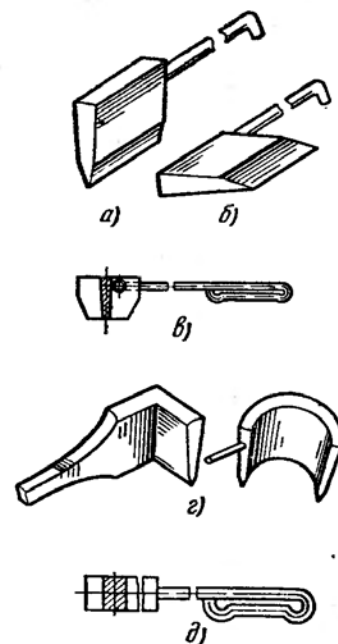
Топоры (а — двусторонний, б — односторонний, в — трапецевидный, г — фасонные) и обсечка (квадрат) — д
